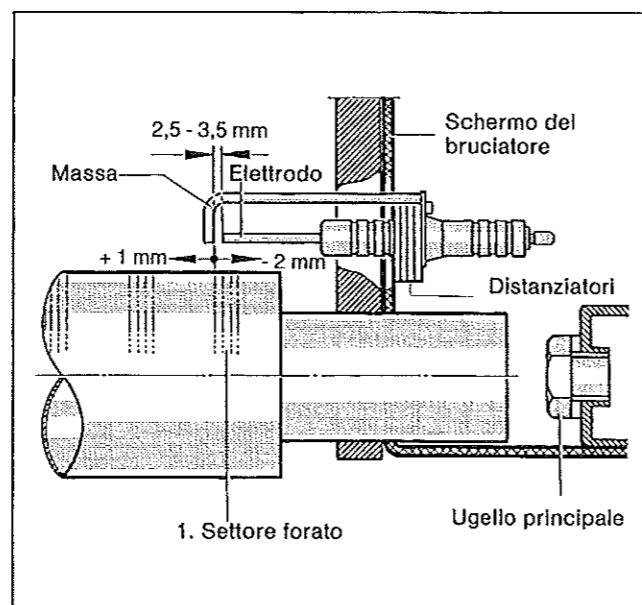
Posizione della scintilla di accensione sul settore forato.
